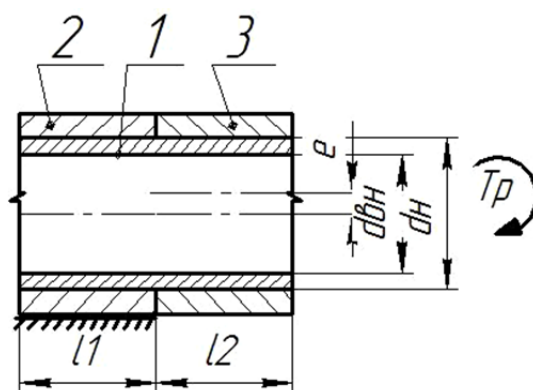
Схема процесса отрезки (1 – труба; 2, 3 – ножи)
